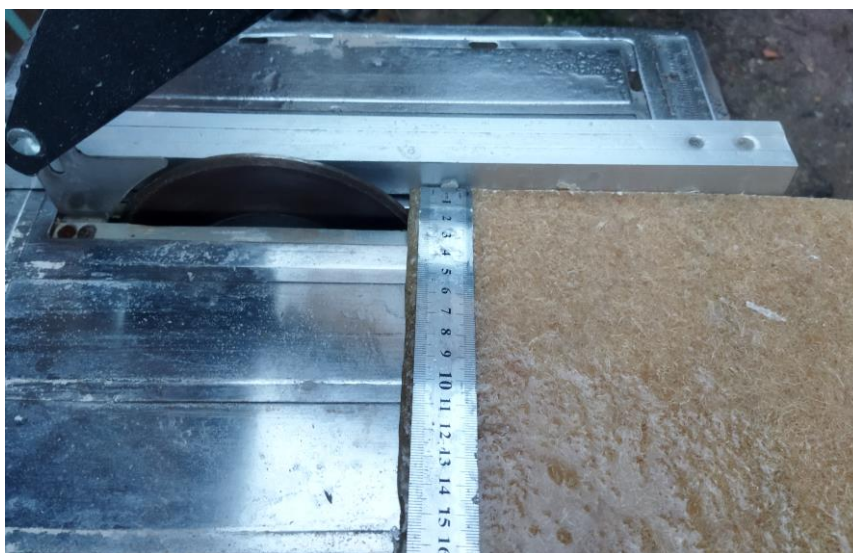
Tronçonneuse à disque diamanté utilisée pour le découpage des plaques bio composites.
